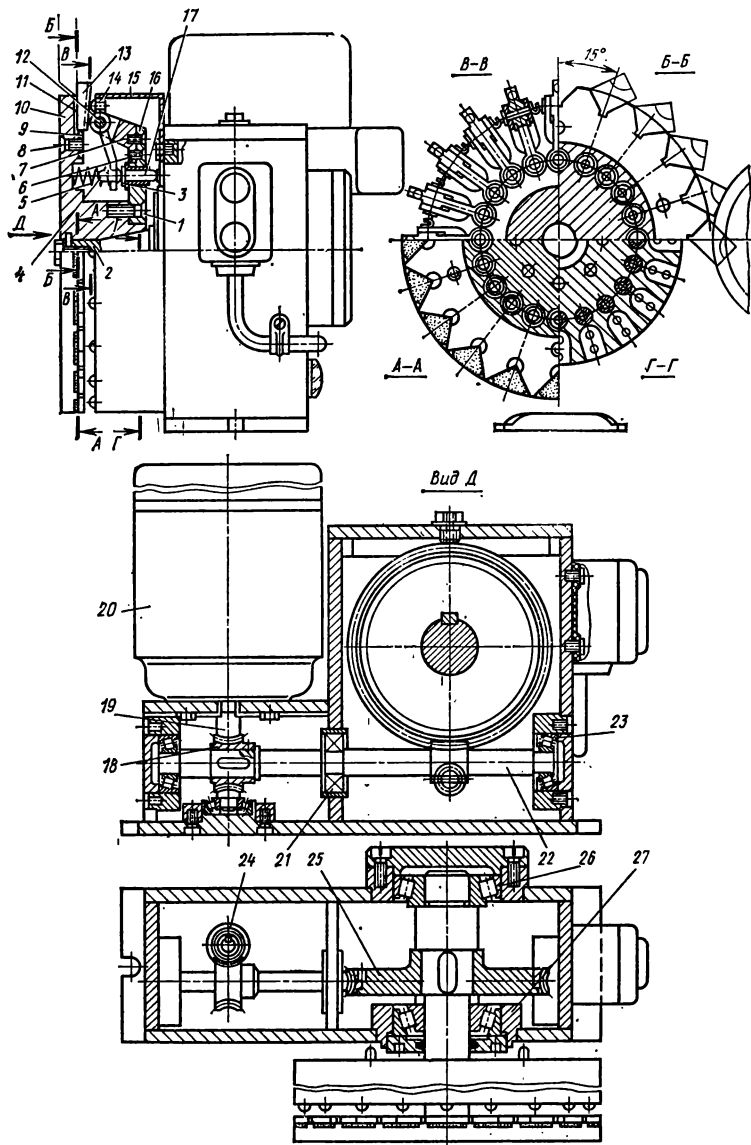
Приспособление для доводки передней поверхности ножей, оснащенных пластинками из твердого сплава
